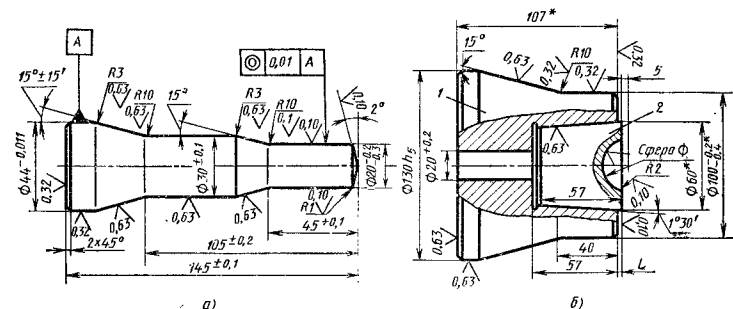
Примеры оформления чертежей рабочего инструмента:
